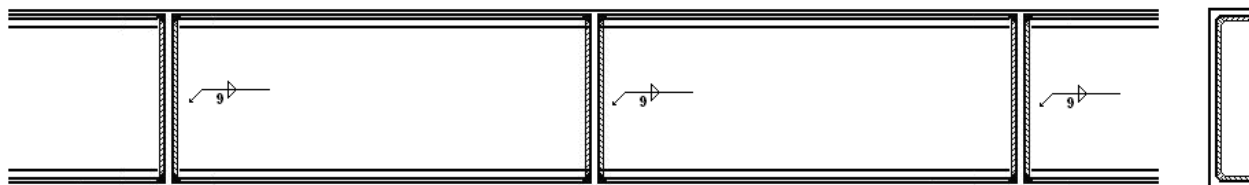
Soldadura dos reforços nas secções de apoio das longarinas e secção central da viga
